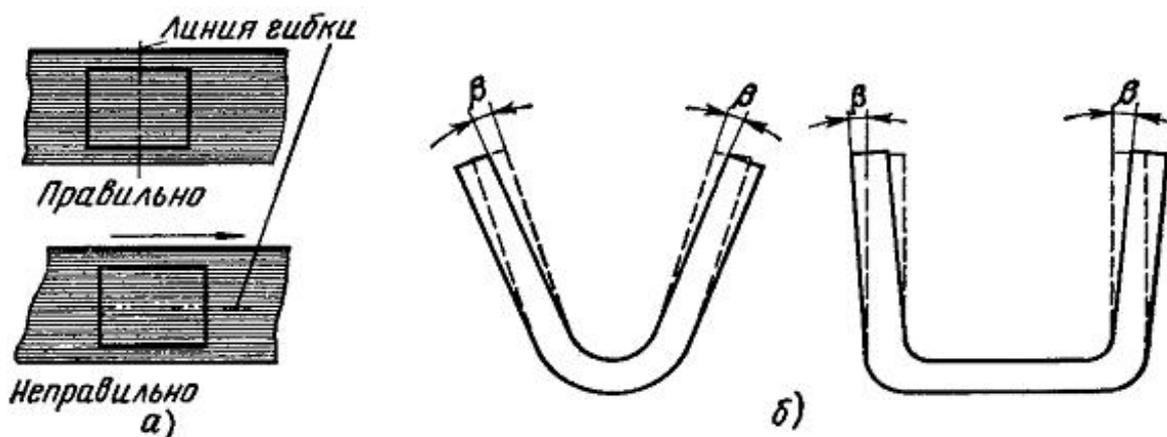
Расположение линий гибки (а) – стрелкой показано направление волокон металла и пружинение (б), β – угол пружинения
